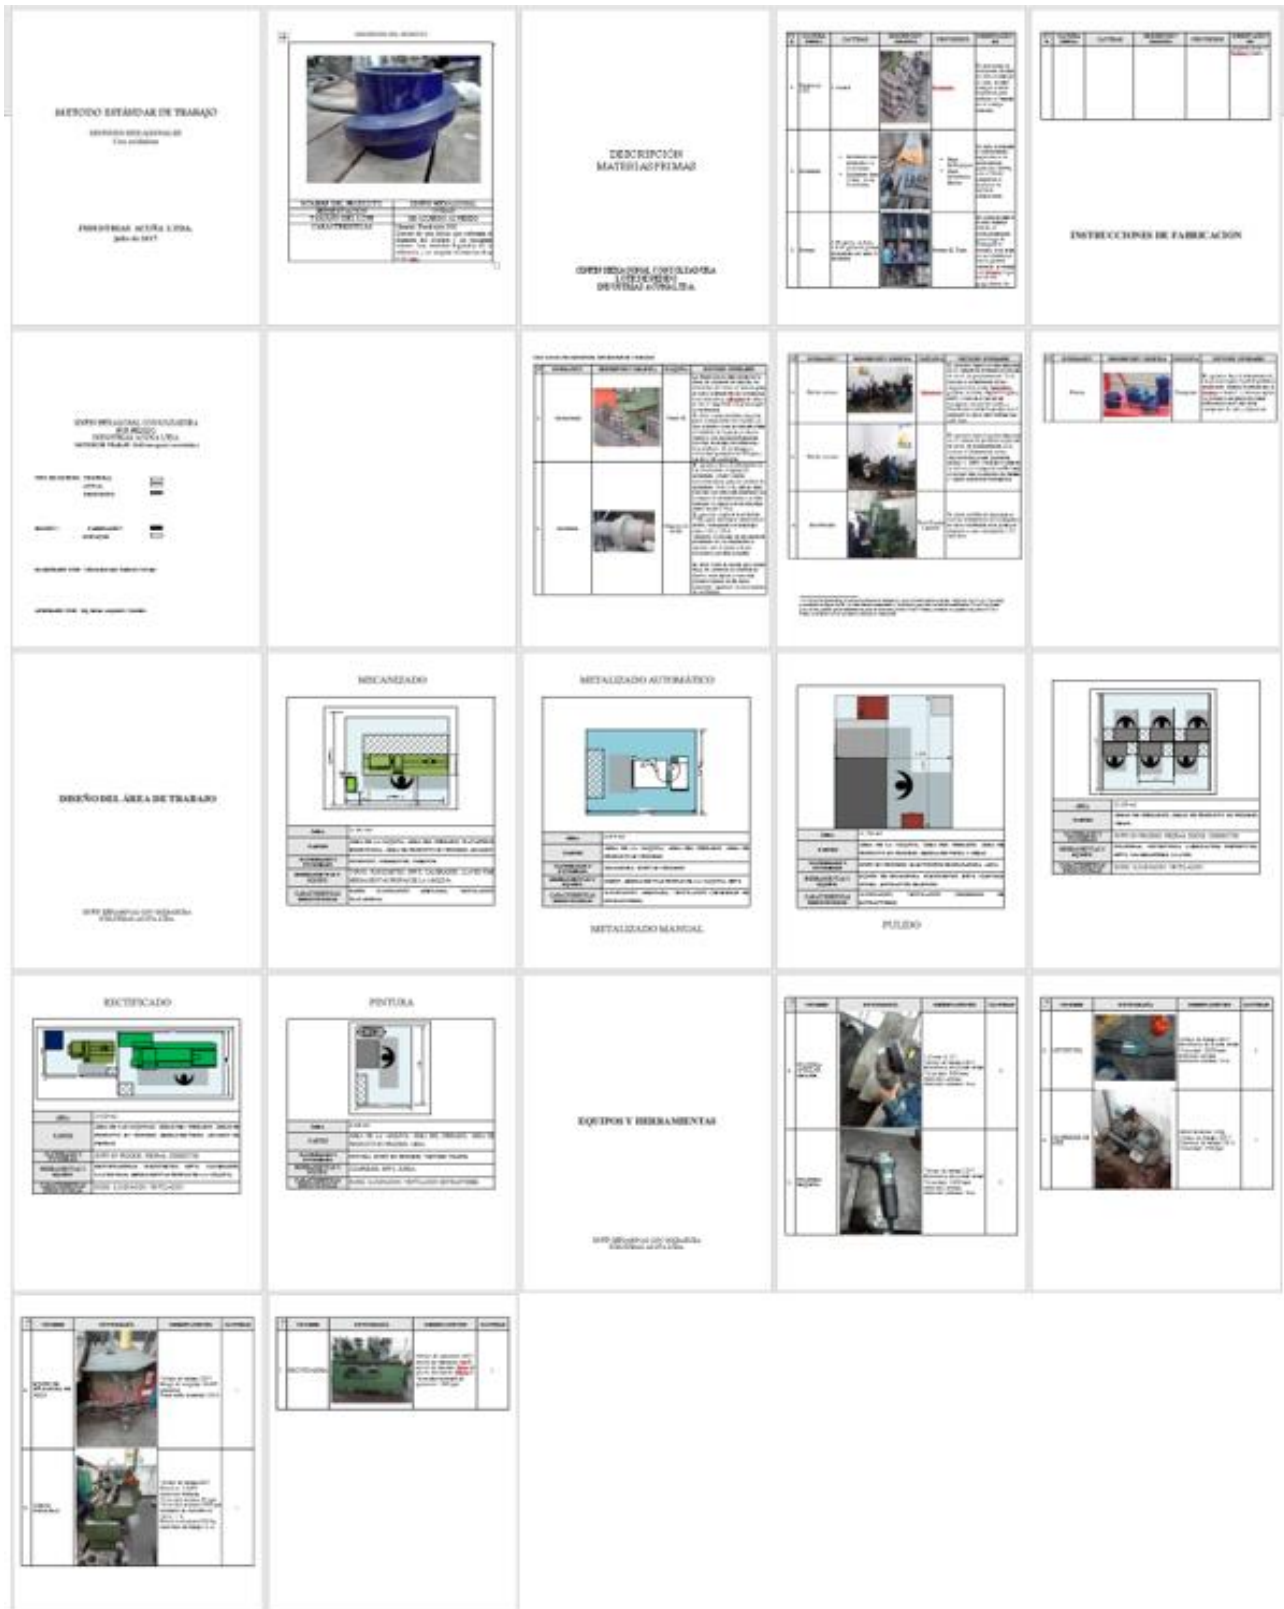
Método estándar-Sinfines hexagonales con soldadura.
